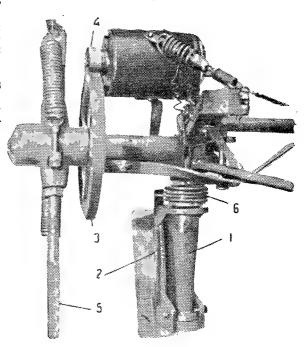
Головка ветроагрегата ПД-2. 1— станина, 2— кроиштейн, 3— чугунный шкив иа втулке, 4— деревянный шкив динамо, 5—крыло, 6—коль- да токопрнемника
